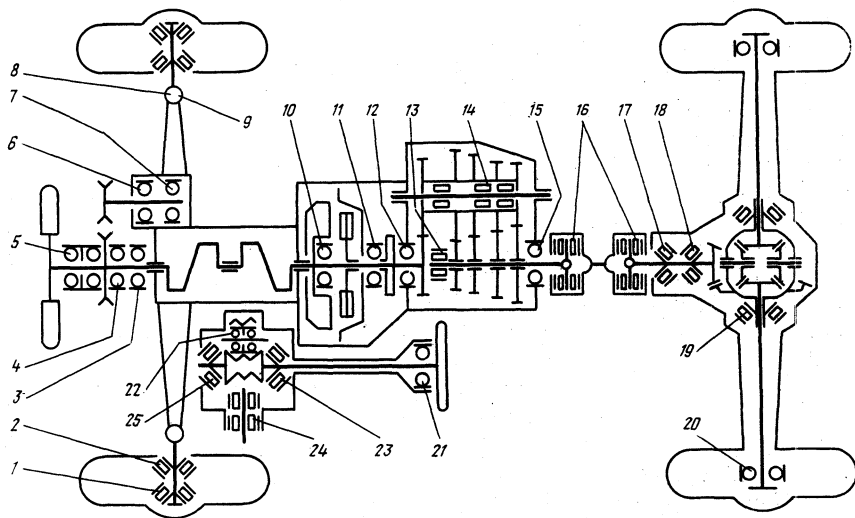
Схема расположения подшипников качения на автомобиле ГАЗ-24 «Волга»:
